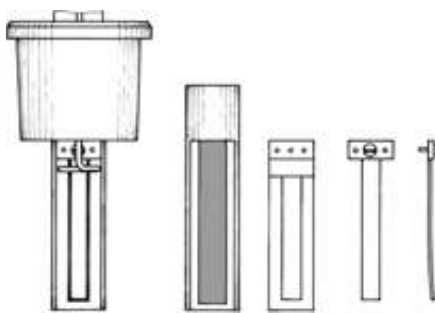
Dibujo de despiece de una boquilla de lengüeta libre.
